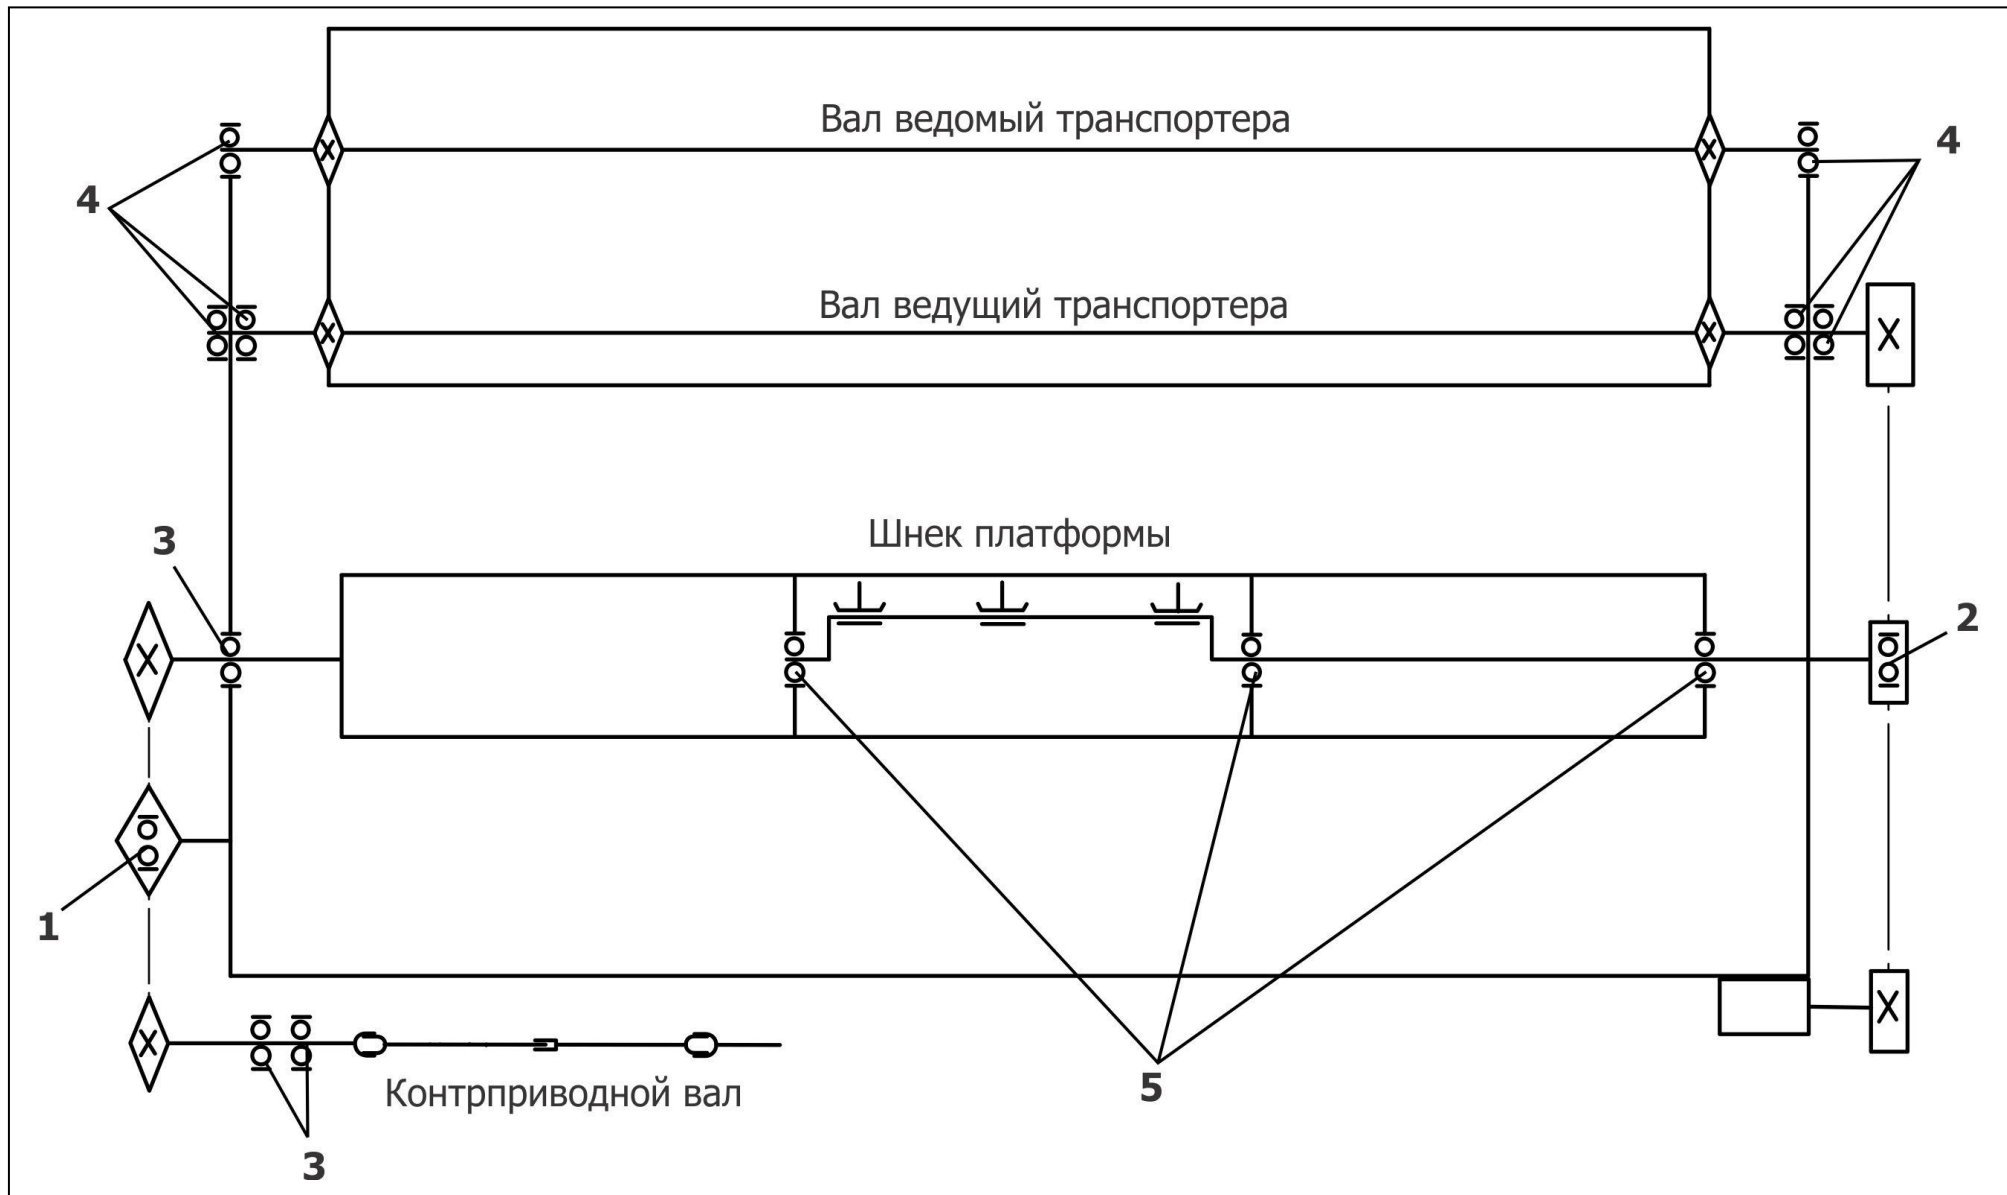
Схема расположения подшипников платформы-подборщика
